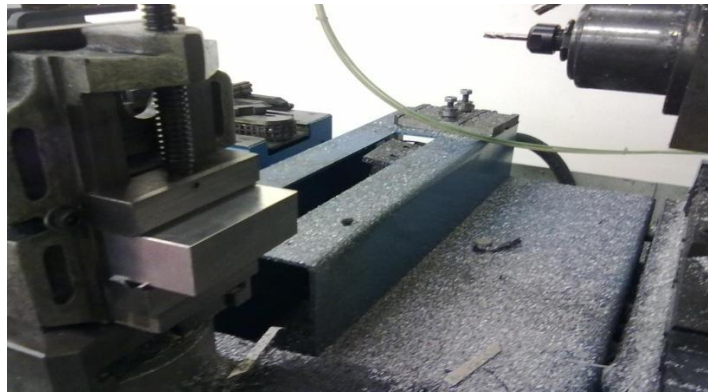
Bloco de alumínio a maquinar fixo na mesa da fresadora de *CNC
